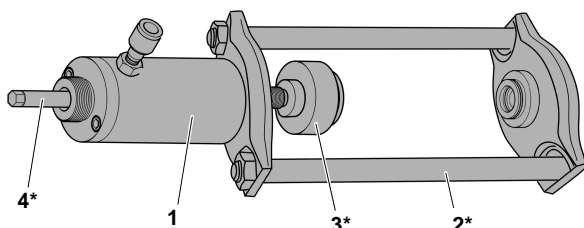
Pressrahmen, Hydraulikzylinder, Druckspindel und Adapter.
